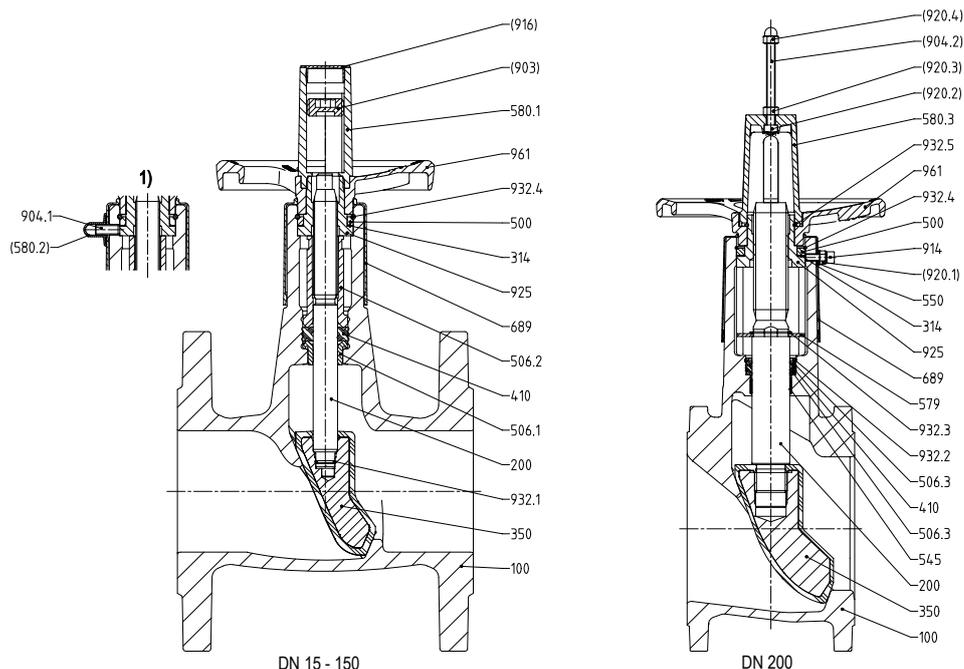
Vistas de sección; 1) dibujadas giradas 90°
